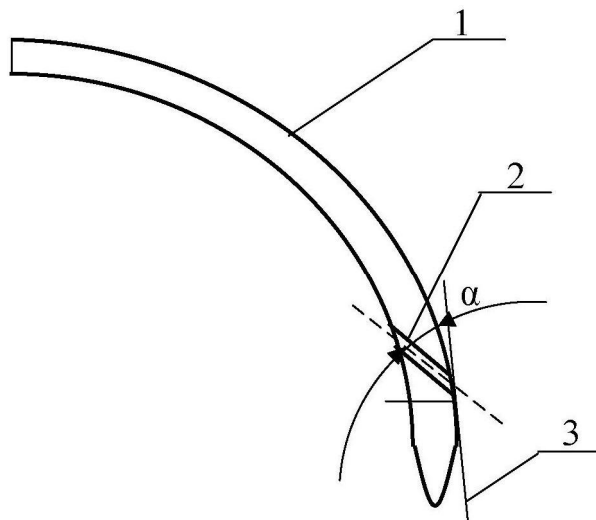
Профіль лопатки: 1- поверхня лопатки; 2 – повздовжня щілина; 3 - дотична
